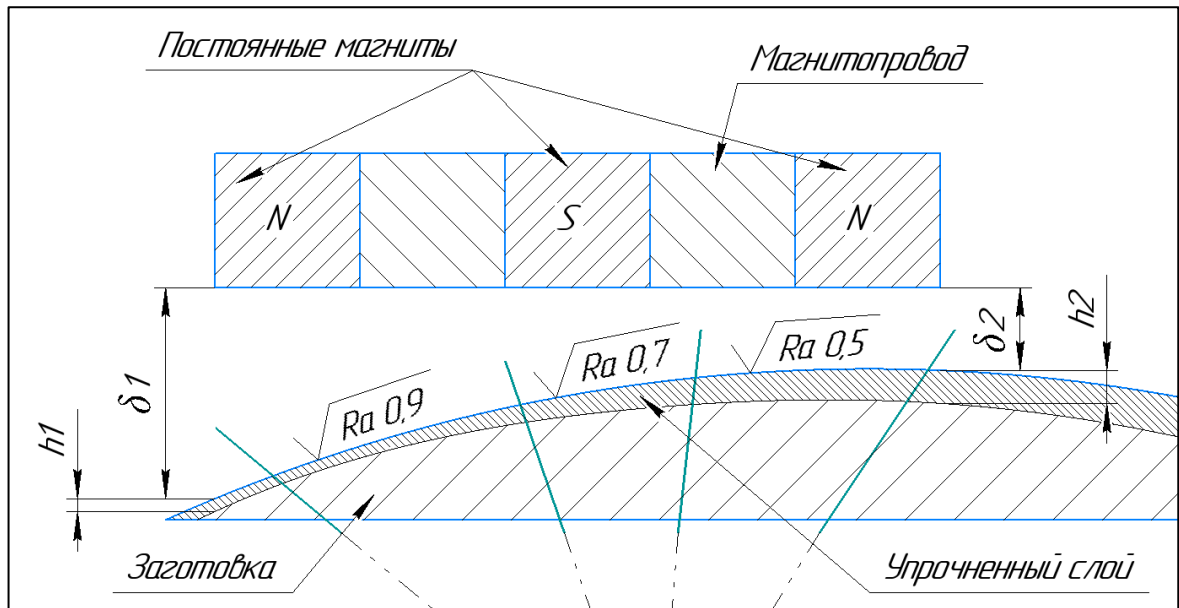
Изменение глубины наклепа и шероховатости при обработке заготовки сферической формы на установке с плоским индуктором, где:
